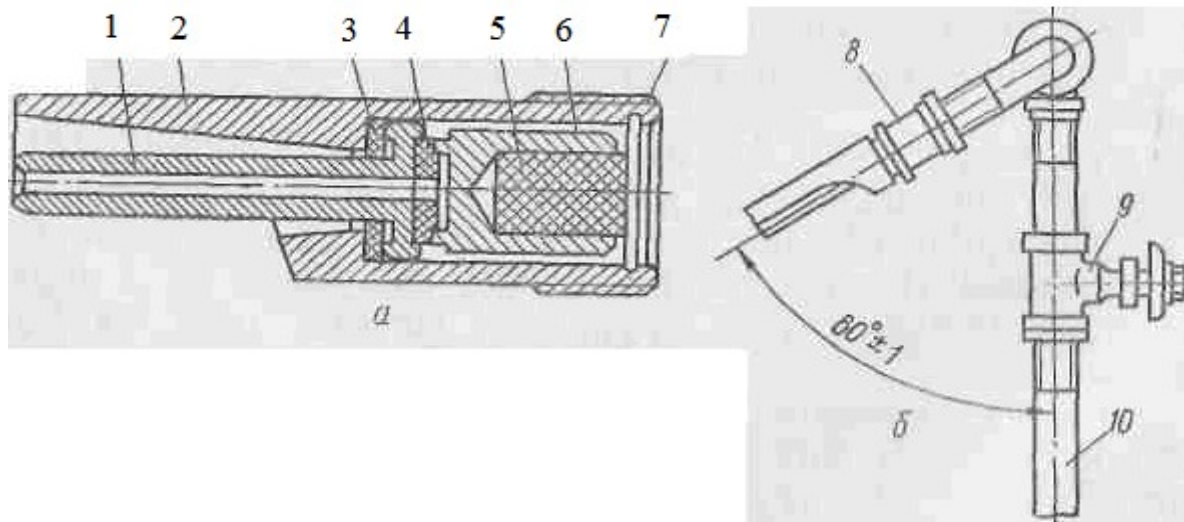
Напувалка соскова ПБС- 1: а - пристрій поїлки; б - схема її установки; 1 - сосок; 2 - корпус; 3,4 - ущільнювальні прокладки; 5 - амортизатор; 6 - клапан; 7 - упор; 8 - муфта; 9 - вентиль; 10 -стojак.
